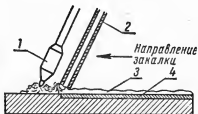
Схема закалики плоской детали кислородно-ацетиленовым пламенем;
